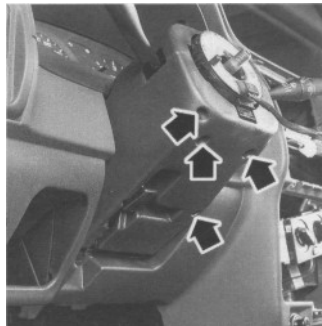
Rozmieszczenie śrub mocowania konsoli środkowej
